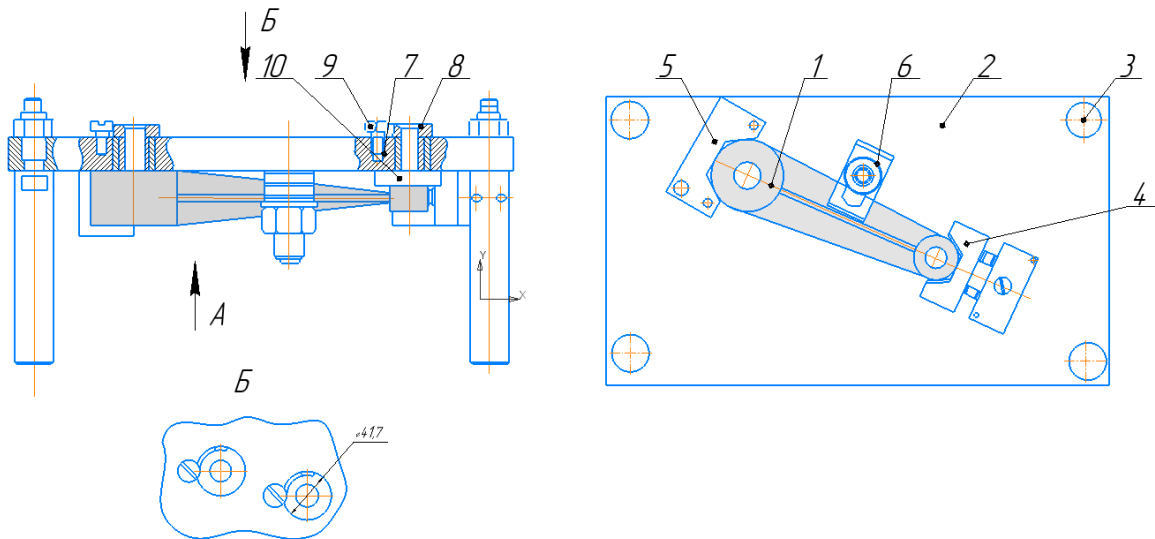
Схема кондуктора: 1 – заготовка; 2 – плита; 3 – стійка;
